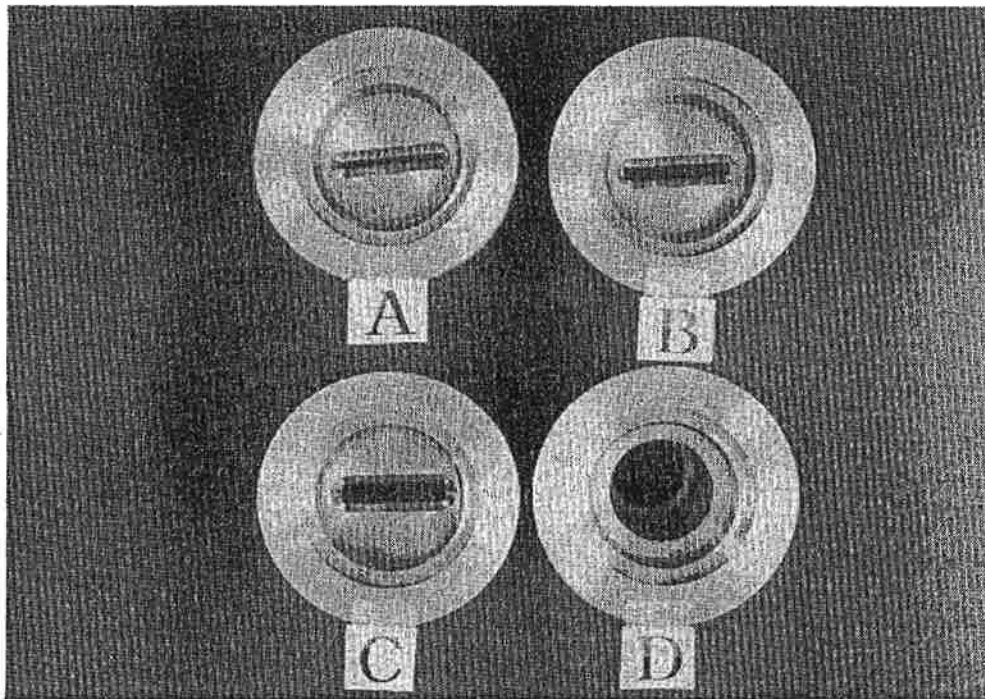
각종 실험용 Die plate의 Breaker plate insert seat
